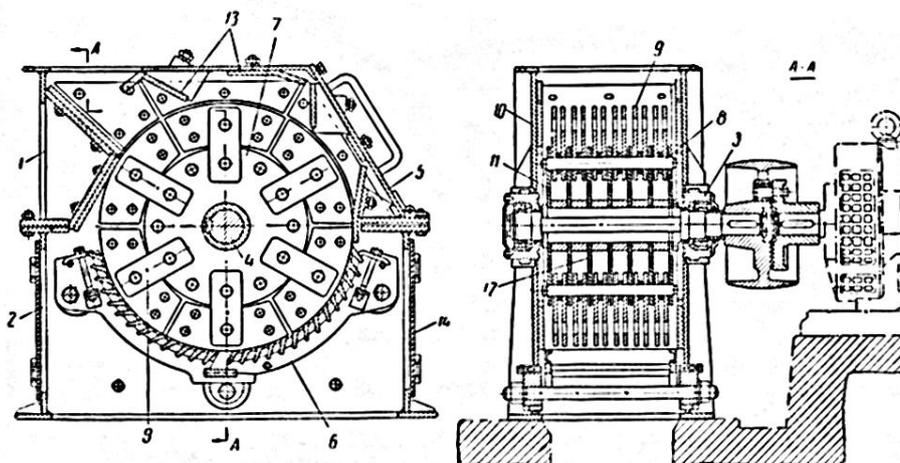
Однороторная молотковая дробилка: 1, 2 - верхняя и нижняя часть корпуса; 3 – подшипники скольжения; 4 – роторный вал; 5 – откидная стенка; 6 – колосниковая решетка; 7 – ротор; 8 – стержни (ось дробящий молотков); 9 – молотки;
